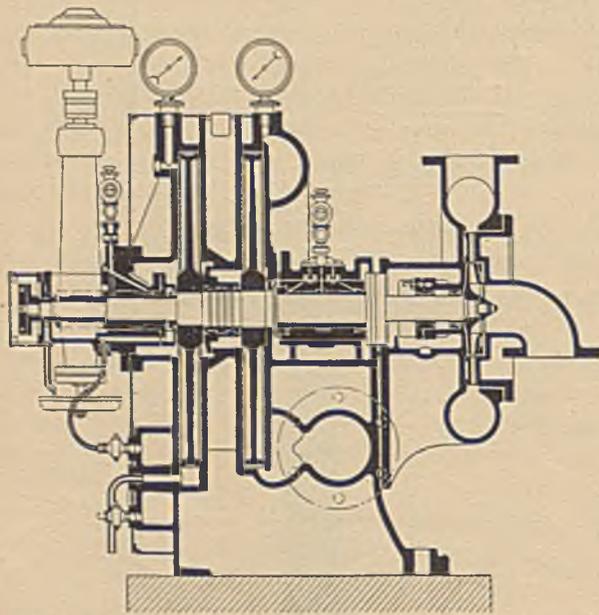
Längsschnitt einer wagrechten Unionturbine.
